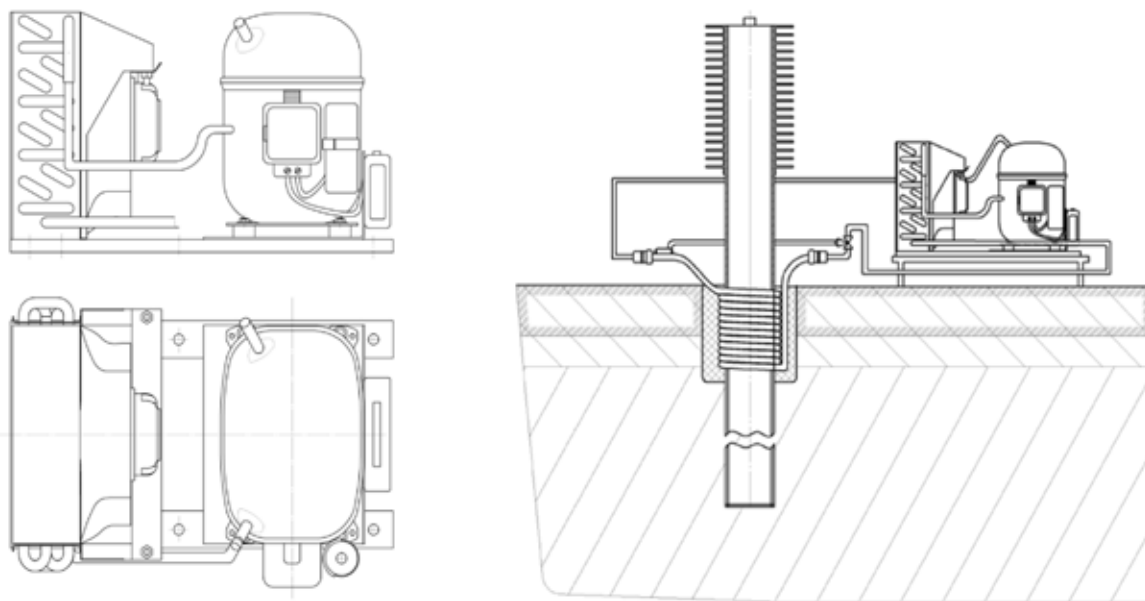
Общий вид компрессорно-конденсаторного агрегата
